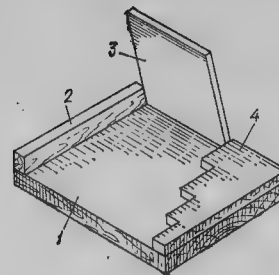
1 — основание; 2 — брусок ограничительный; 3 — плитка; 4 — планка калибровочная
